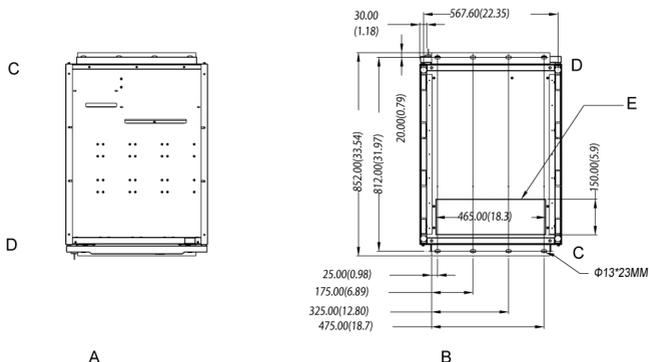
Габаритные размеры шкафа ИБП на 160-200 кВА (вид сверху и снизу)
